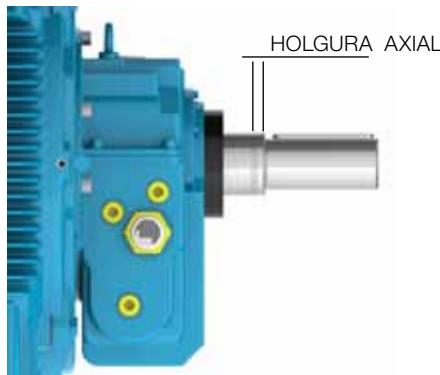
Holgura axial en motor equipado con cojinete de deslizamiento.
